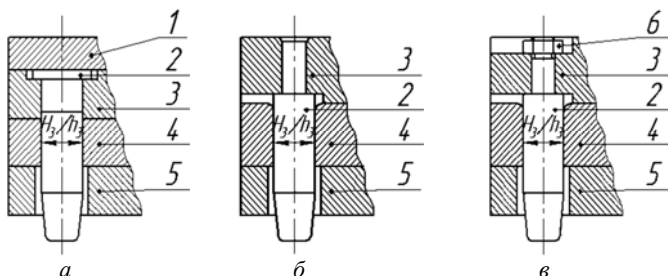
Примеры установки и конструкции направляющих штырей: 1 – подкладная плит; 2 – направляющий штырь; 3 – подвижная матрица; 4 – матрица неподвижная; 5 – неподвижная плита основания; 6 – гайка
